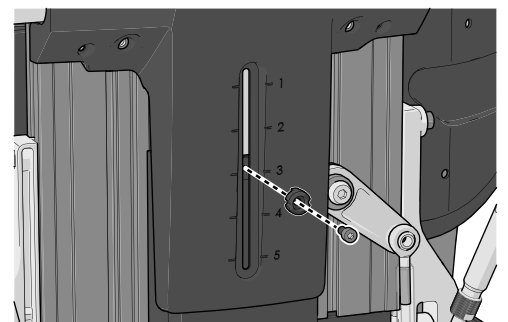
Der Kunststoffknopf ist mit einer Schraube befestigt.
